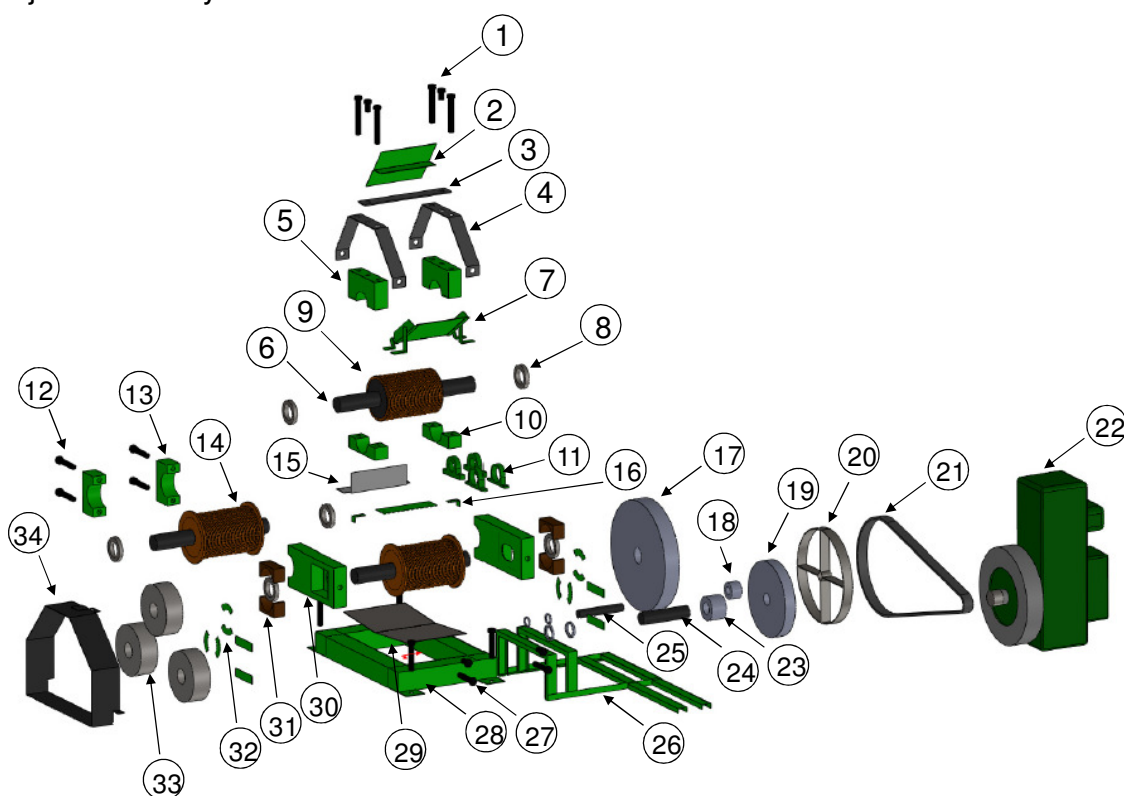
Despiece de la máquina de molienda de caña junto a la caja reductora y motor
